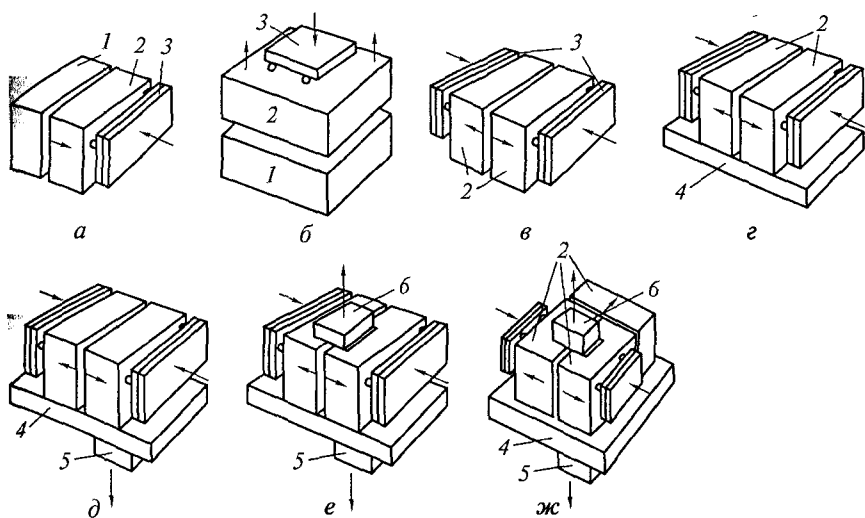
Типы кокилей для универсальных кокильных машин (стрелки — направление движения деталей кокиля):
